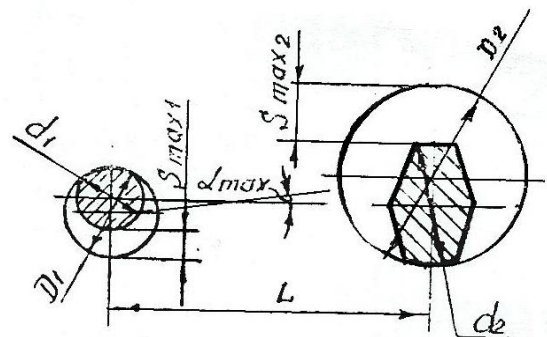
Схема к расчету погрешности базирования детали «Корпус».
